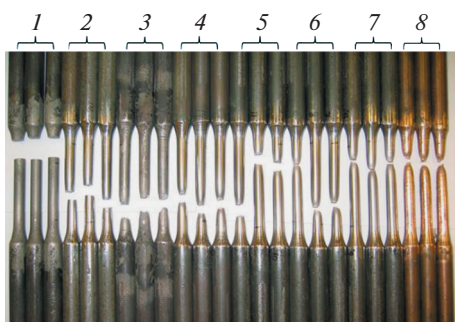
Образцы прутков, после испытаний: 1 – Сталь 65Г (закаленная); 2 – Сталь 65Г; 3 – Сталь 30ХГСА (закаленная); 4 – Сталь 30ХГСА; 5 – Сталь 45; 6 – Сталь 20; 7 – Сталь 3; 8 – Бронза БрОЦ4-3.
